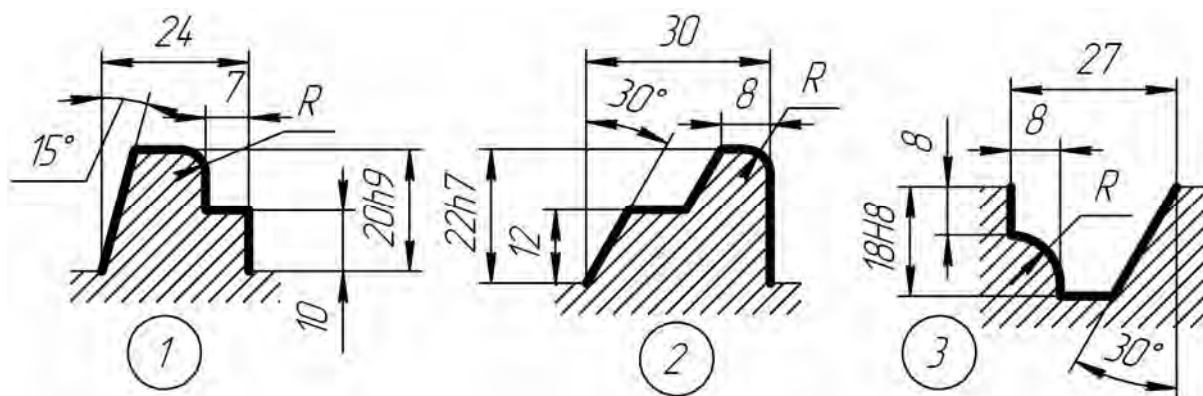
Эскизы деталей для расчета фасонных фрез
